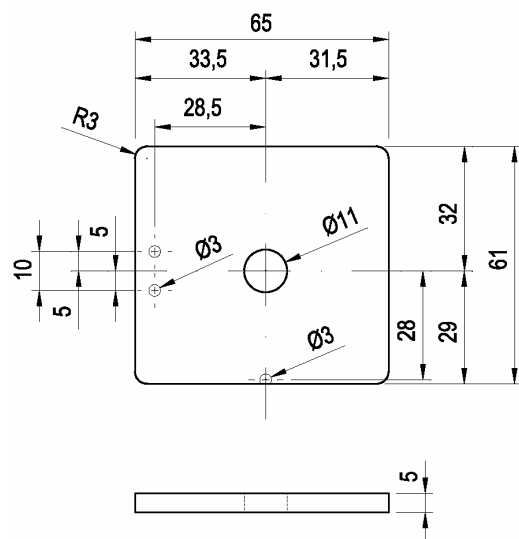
Pieza Omega. Placa de soporte 61x65x5 mm.
